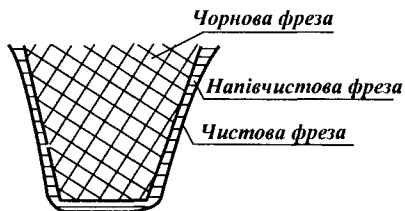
Схема утворення зуба провідного ротора компресора комплектом фрез.
